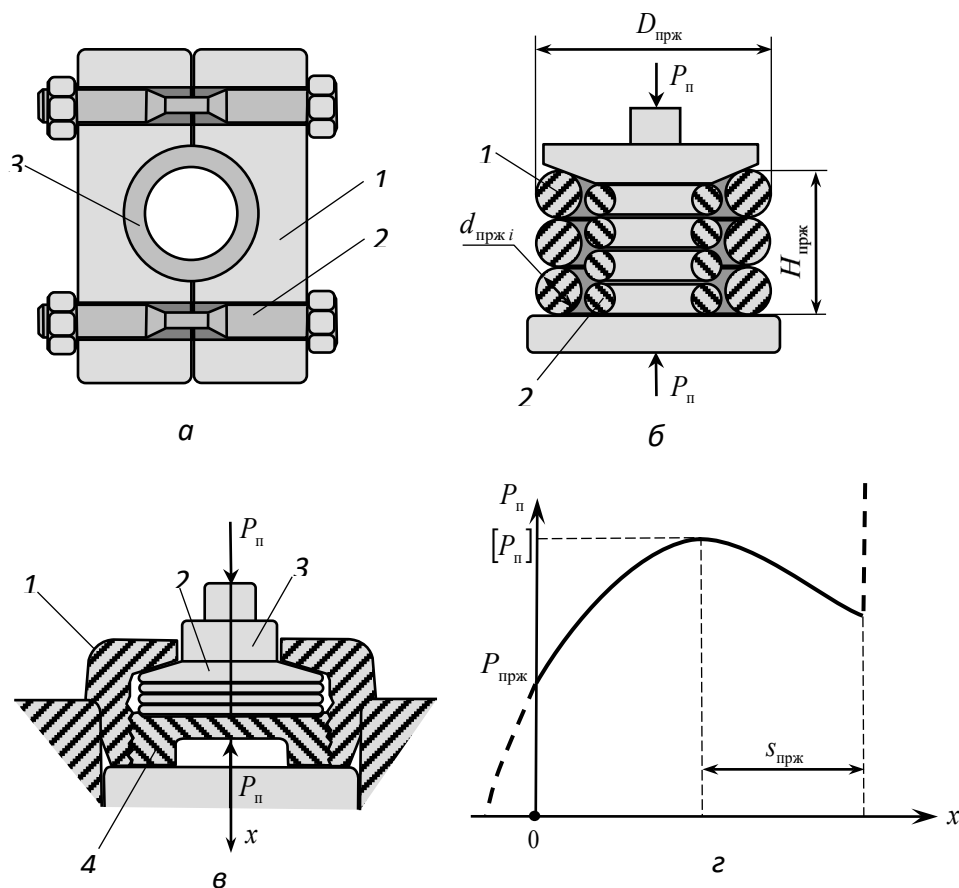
Запобіжні пристрої: *a* — з руйнівними болтами: 1 — пластина; 2 — поглиблення під клин; 3 — болт; *б* — з паралельно працюючими пружинами: 1, 2 — пружини; *в* — з тарільчастими пружинами: 1 — напрямний шток; 2 — пакет тарільчастих пружин; 3 — фланець циліндра; 4 — опорна гайка; *z* — «м'яка» характеристика жорсткості пакета тарільчастих пружин ($d_{\text{прж } i}$ — діаметр поперечного перетину i — й пружини; $D_{\text{прж}}$ — зовнішній діаметр пакета пружин; $P_{\text{прж}}$ — сила початкової затяжки пакета пружин; $H_{\text{прж}}$ — висота пакета стиснутих пружин; $s_{\text{прж}}$ — ход пружини)
